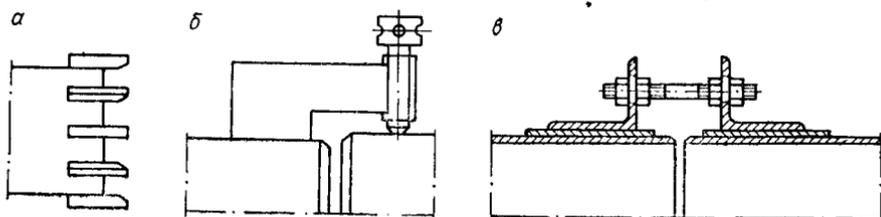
Приспособления для подгонки стыков: а — направляющие планки; б — приварная трубка; в — болтовое стяжное приспособление.
